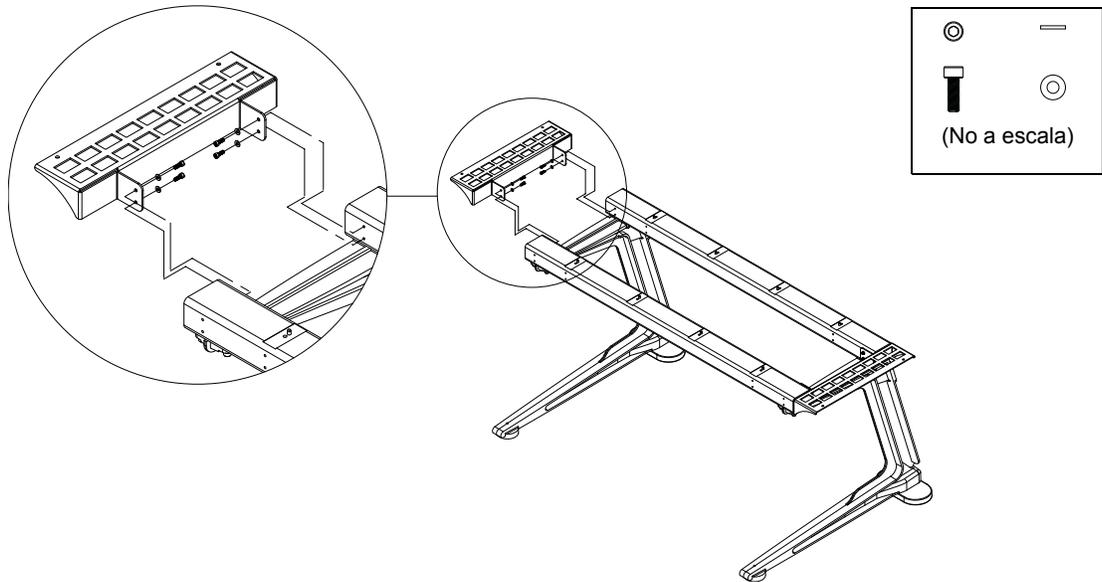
Unir la repisa izquierda (la repisa derecha aparece ya montada)
